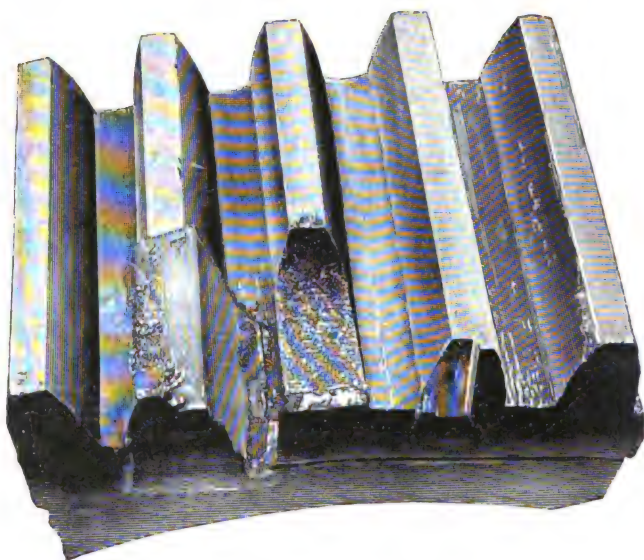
Zahnradabschnitt mit abgebrochenem Zahn mit unbearbeiteter und bearbeiteter Aufschweissung.
